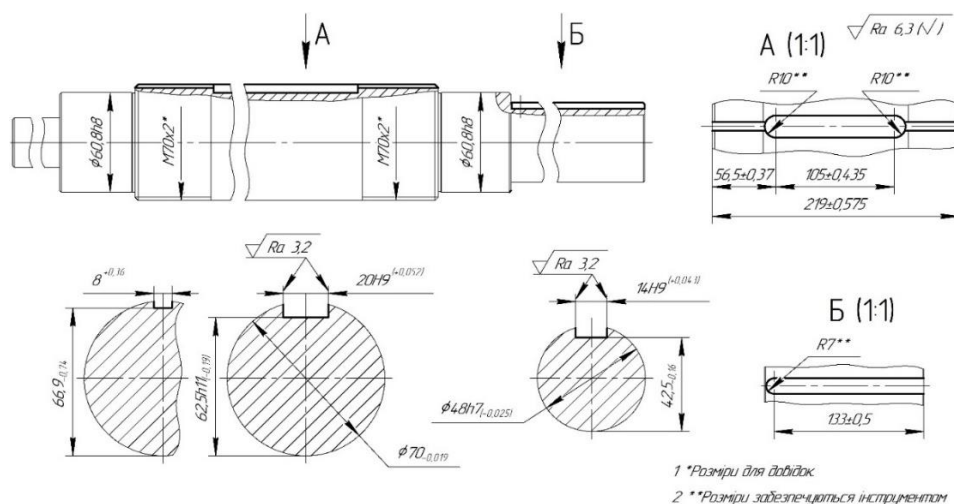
Ескіз заготовки на операції 025 «Фрезерна з ЧПК»
